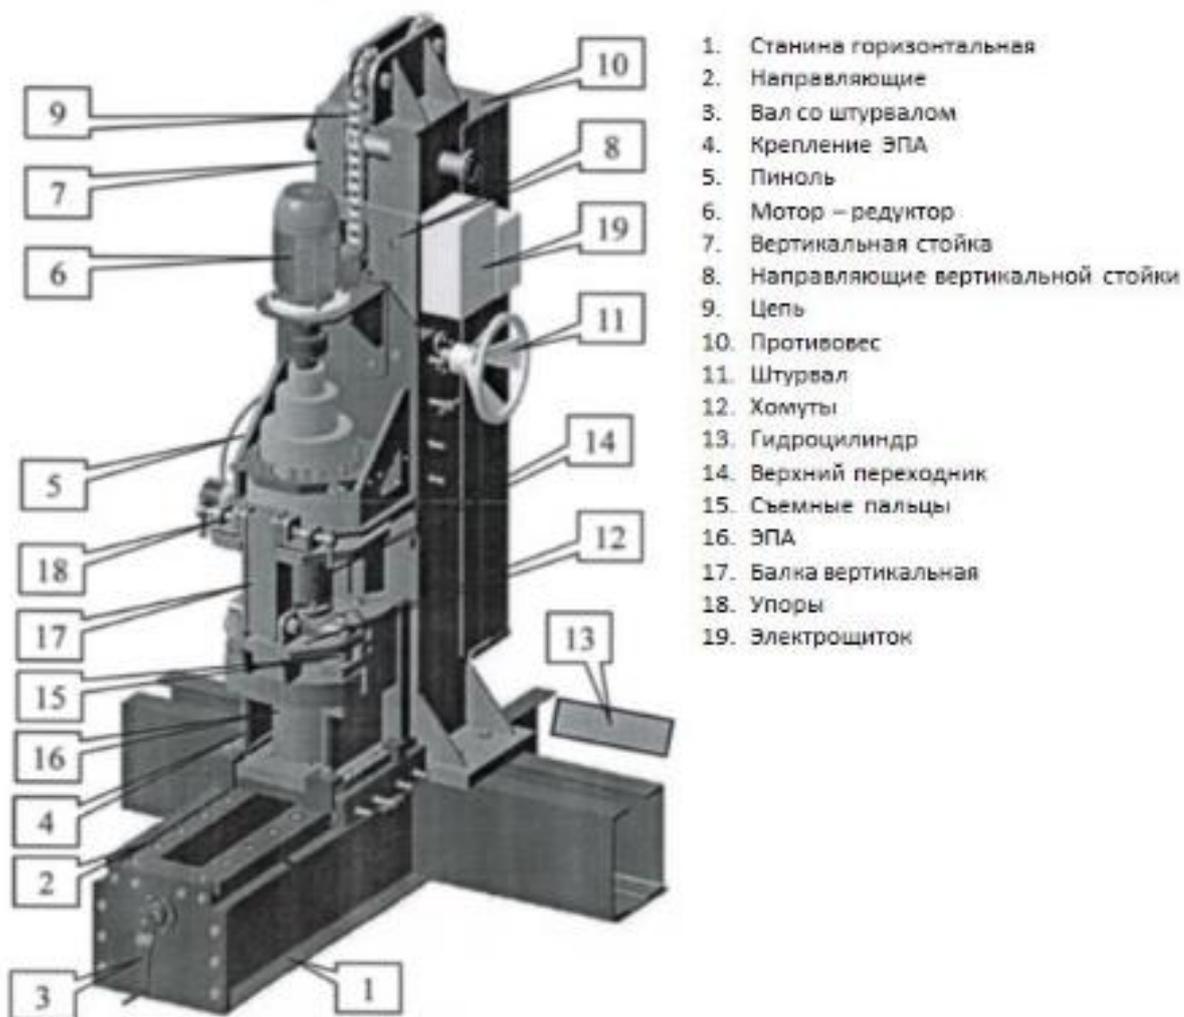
Установка для разборки и сборки эластомерного поглощающего аппарата в аксонометрии
